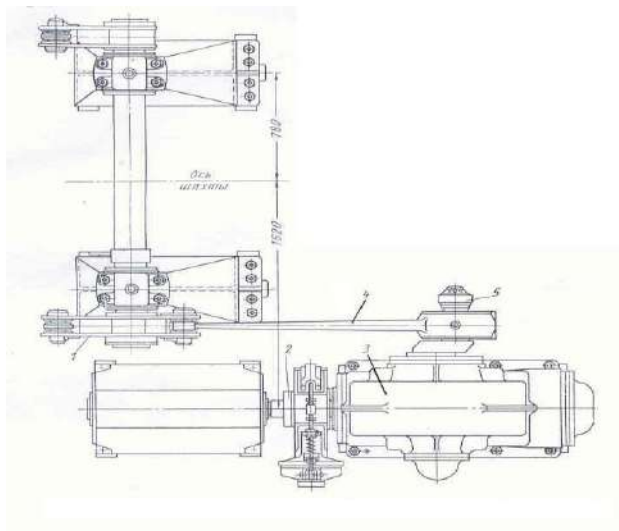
Привод механізму управління великими кліщами (вид зверху).
